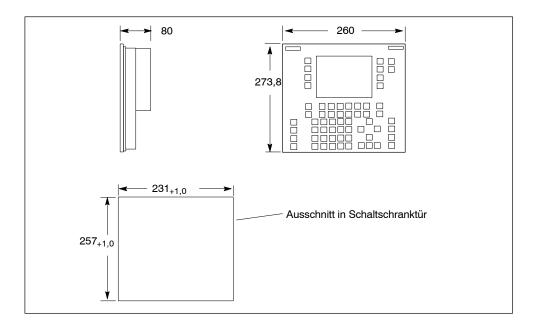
Maßbilder für das C7-635 Key (Maße in Millimeter)
